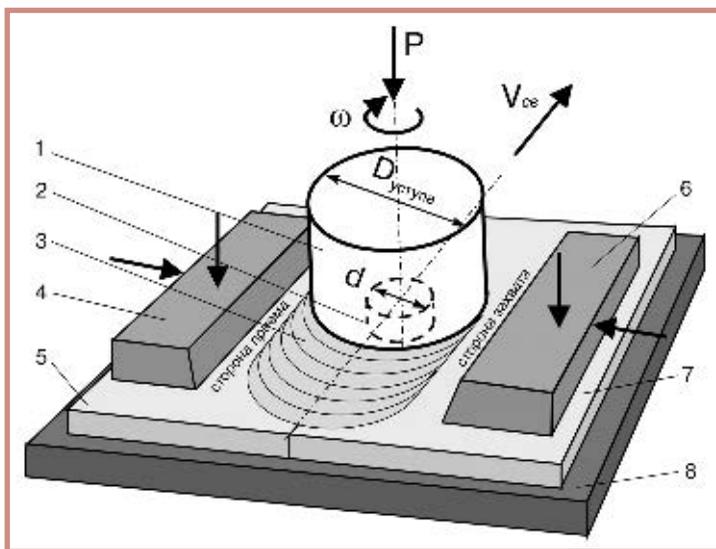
Схема выполнения СТП: 1 — сварочный инструмент; 2 — наконечник сварочного инструмента; 3 — сварной шов; 4, 6 — прижимные планки; 5, 7 — свариваемые заготовки; 8 — технологическая подкладка (ω — скорость вращения сварочного инструмента; $V_{св}$ — скорость сварки; $D_{уст}$ — диаметр опорной поверхности уступа сварочного инструмента; P — осевое давление сварочного инструмента на свариваемые заготовки)
